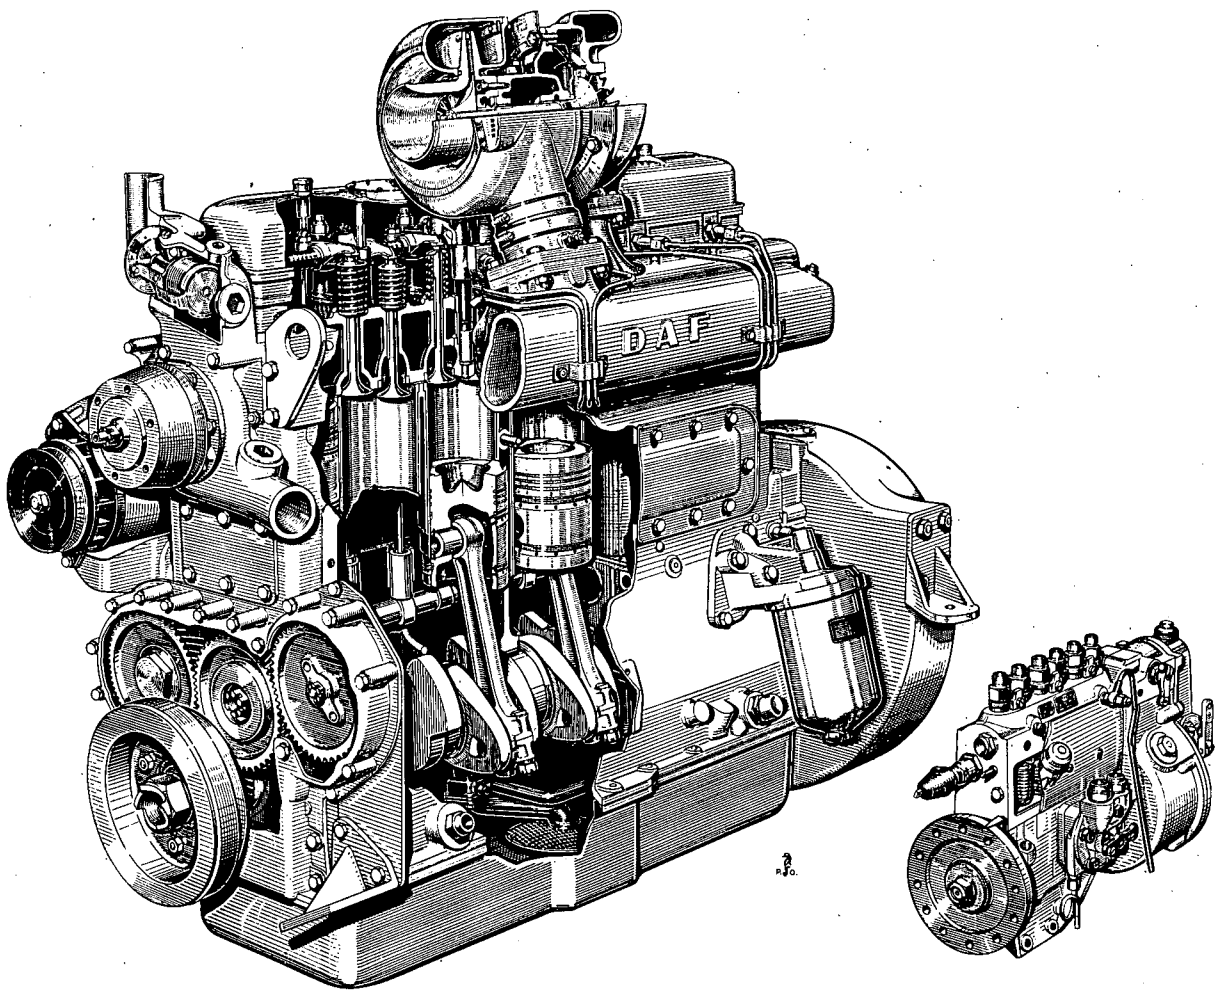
De DAF DS 575 dieselmotor met Holset turbocompressor.
